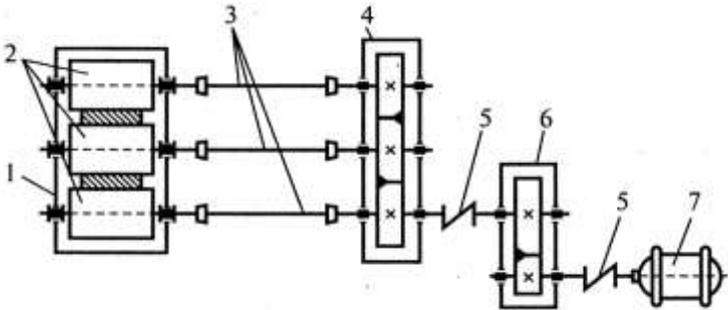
Кинематическая схема прокатного стана: 1 – рабочая клетка, 2 – валки, 3 – шпиндели, 4 – шестеренная клетка, 5 – муфты, 6 – редуктор, 7 – электродвигатель
